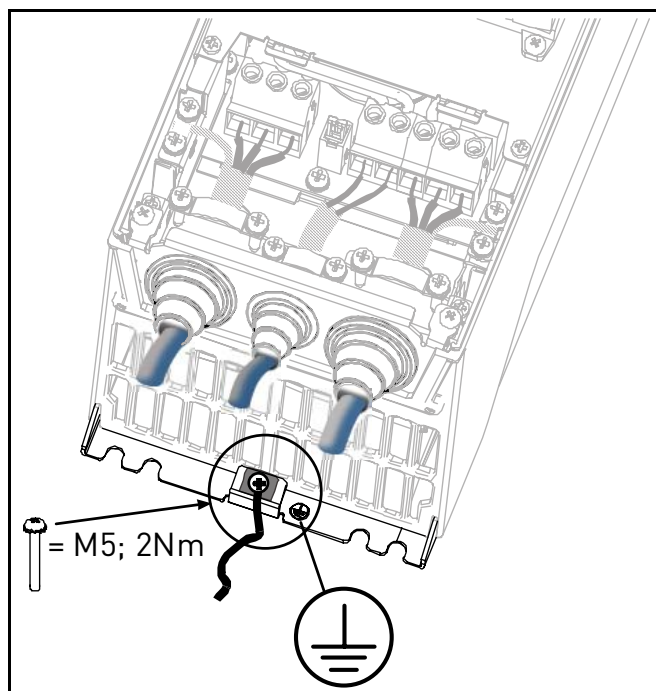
Дополнительный соединитель защитного заземления (12 мм)
